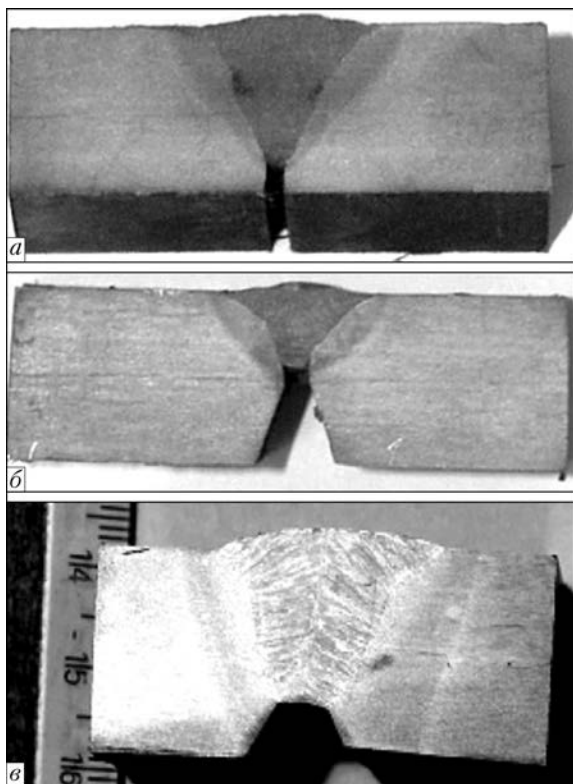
Типичные макрошлифы, изготовленные из технологических проб «жесткая обварка» стали 06ГБД: а, б — механизированная сварка в защитных газах соответственно V- и X-образная разделка кромок толщиной 12 мм; в — автоматическая сварка под флюсом (X-образная разделка кромок толщиной 20 мм)
